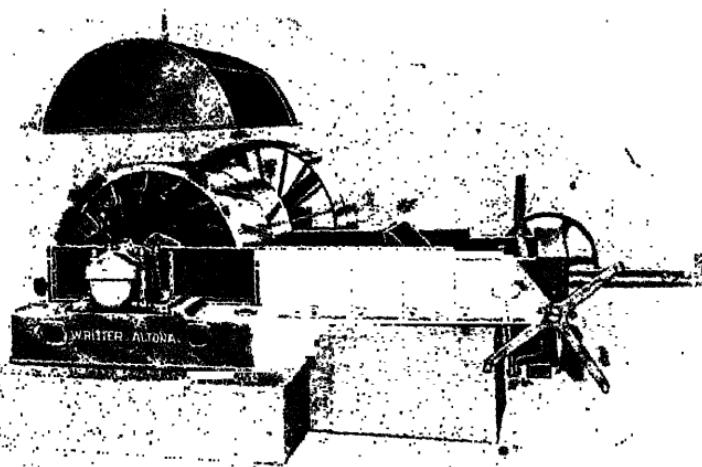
Raspelmaschine der Maschinenfabrik W. Ritter in Altona bei Hamburg.
